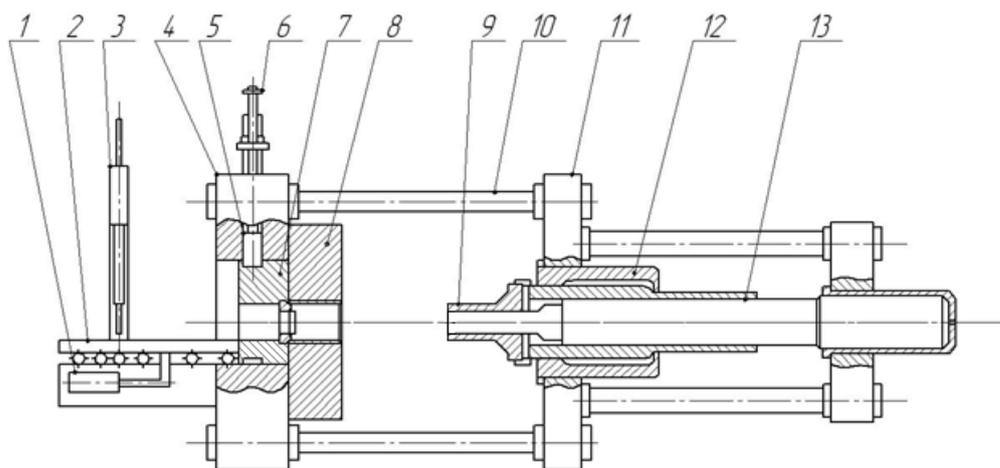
Схема трубопровильного пресса с мундштучным матрицедержателем: 1–гидроцилиндр мундштука; 2–приемный стол; 3–нож; 4–передняя поперечина; 5–затвор мундштука; 6–гидроцилиндр затвора; 7–мундштук; 8–контейнер; 9–пресс-штемпель; 10–колонны; 11–задняя поперечина; 12–главный цилиндр; 13–прошивное устройство.
